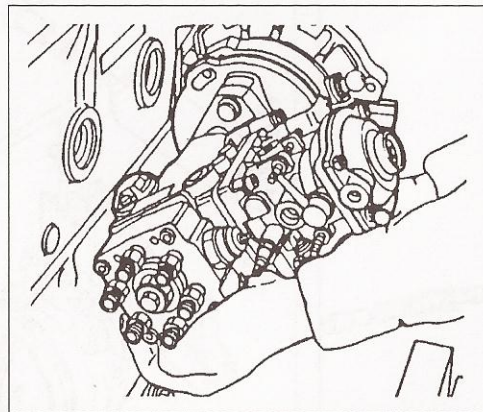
Установка ТНВД на двигатель. При присоединении ТНВД к двигателю рекомендуется расположить его так, чтобы шлицы оказались напротив друг друга.
